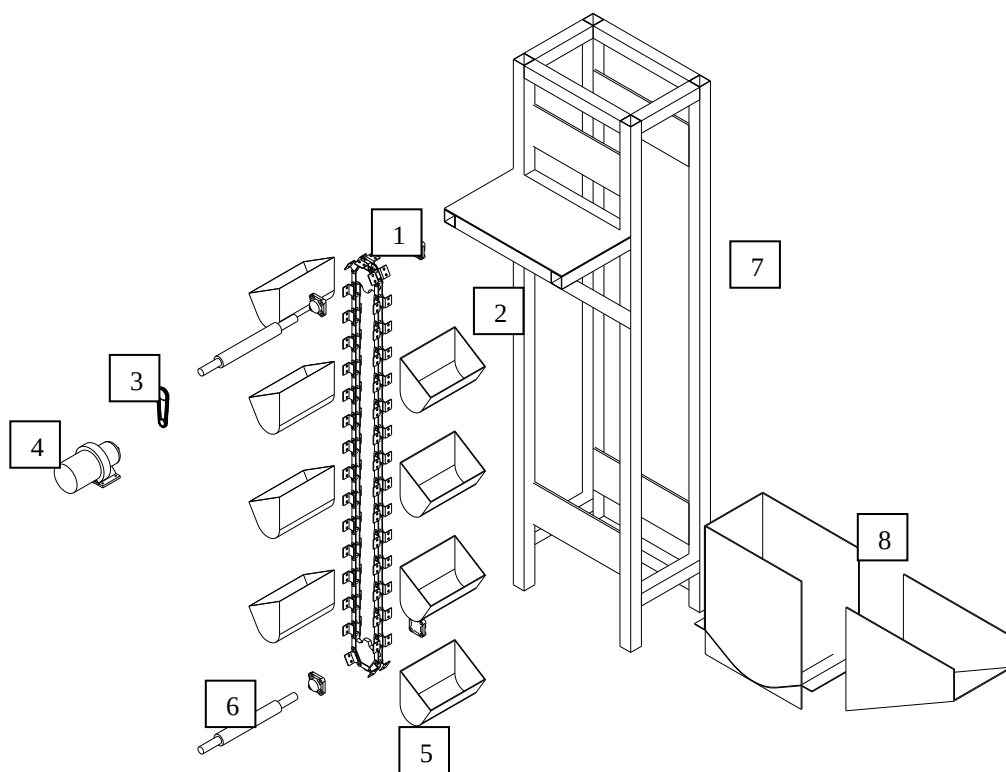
Elevador de cangilones. Fuente. Propia.
